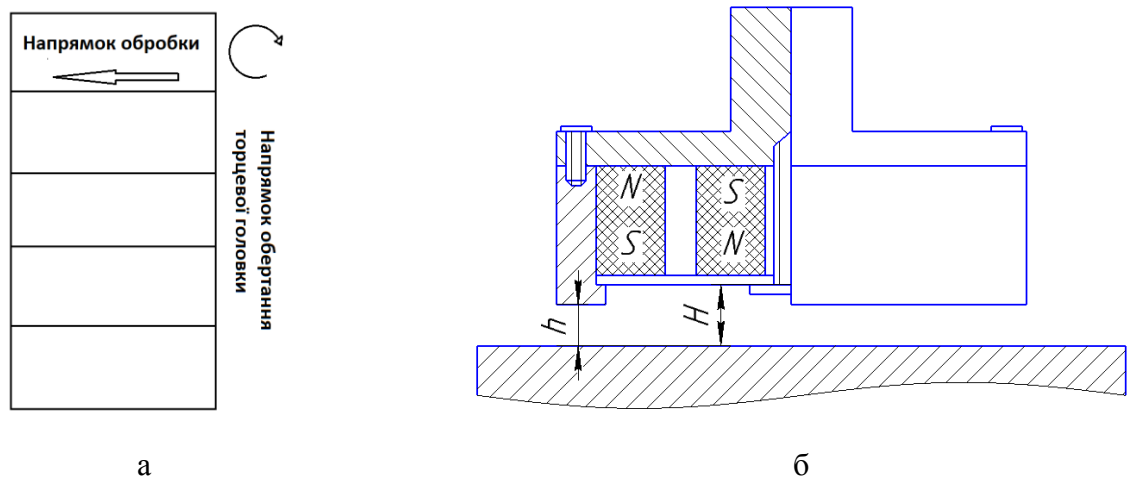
а – Схема напрямків обробки поверхні заготовки, б – Загальна схема обробки, де H – висота між магнітом і поверхнею обробки, h – висота між торцевою поверхнею та поверхнею обробки
